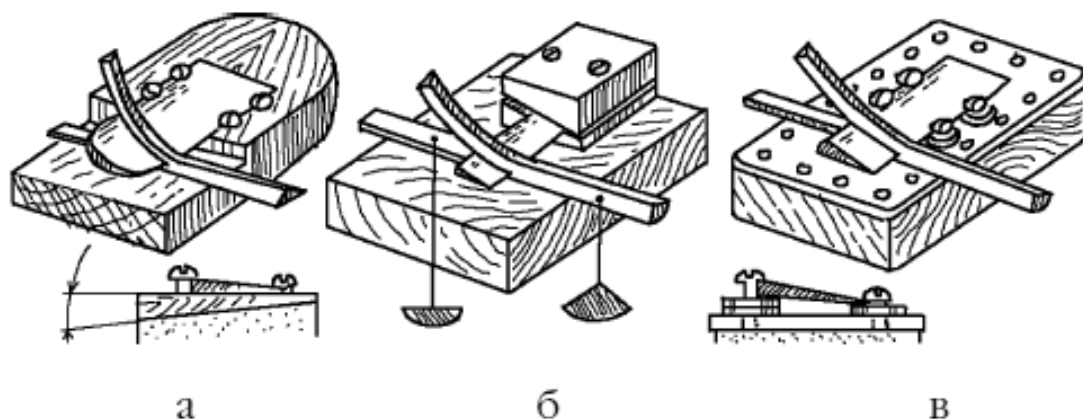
Шриф: а – на основе бруска; б – с прижимной колодкой; в – из деталей детского конструктора
